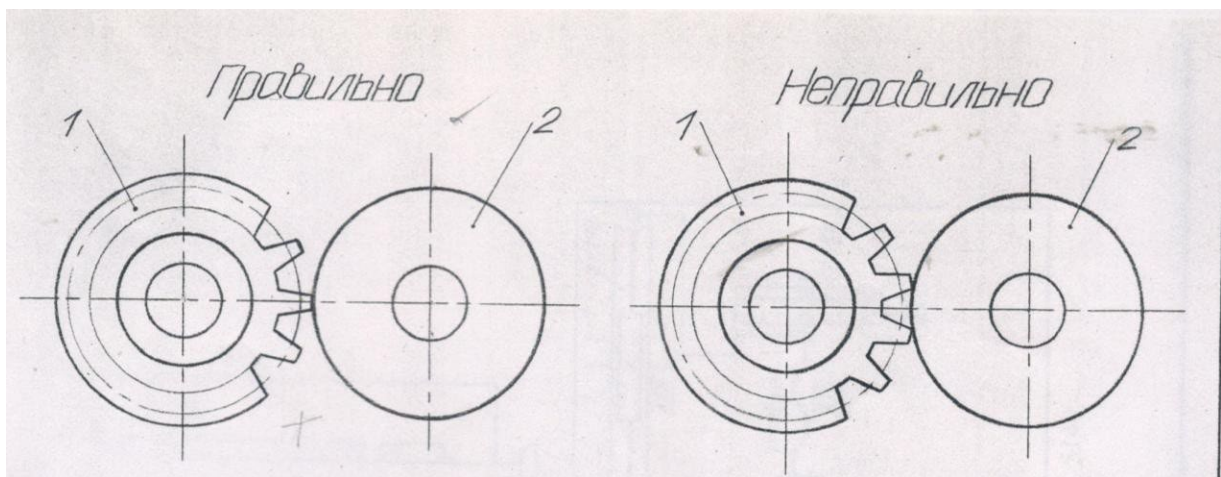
Установка долбяка 91) относительно заготовки (2) перед
